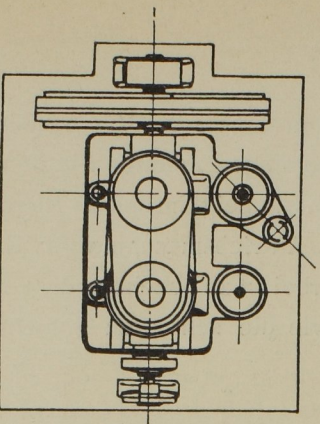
Grundriss. Massst. 1:125.
